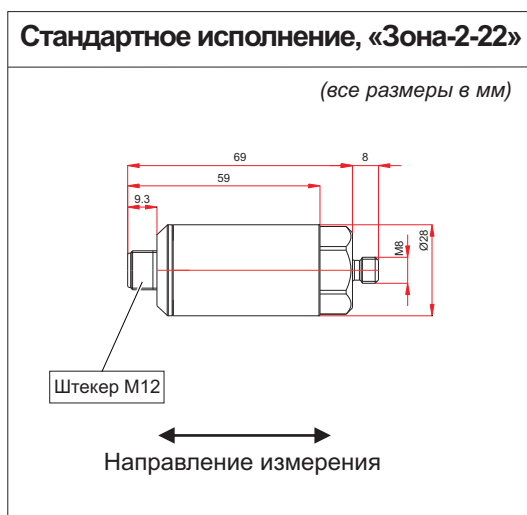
Размеры корпуса и направление измерения: стандартное исполнение, «Зона-2-22».
